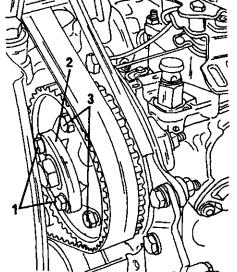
Зубчатый шкив топливного насоса высокого давления.
